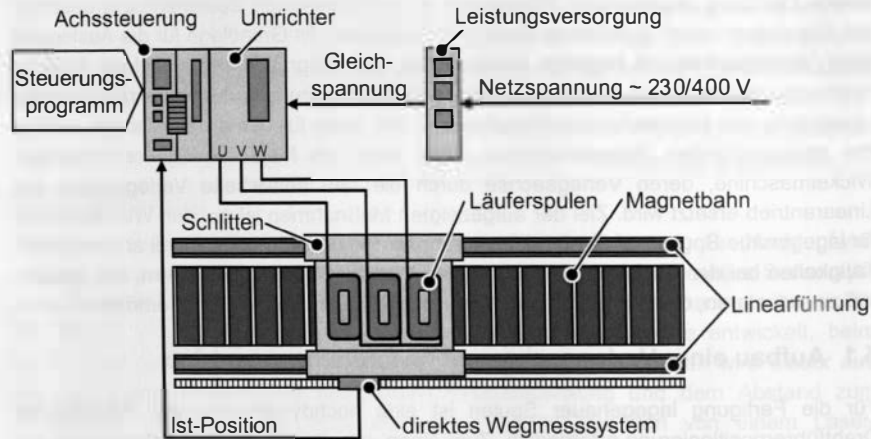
Aufbau einer Vorschubachse mit Linearmotor
